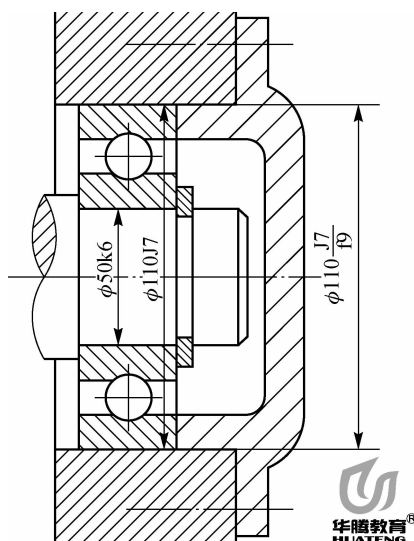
箱体孔与滚动轴承和轴承端盖的配合
